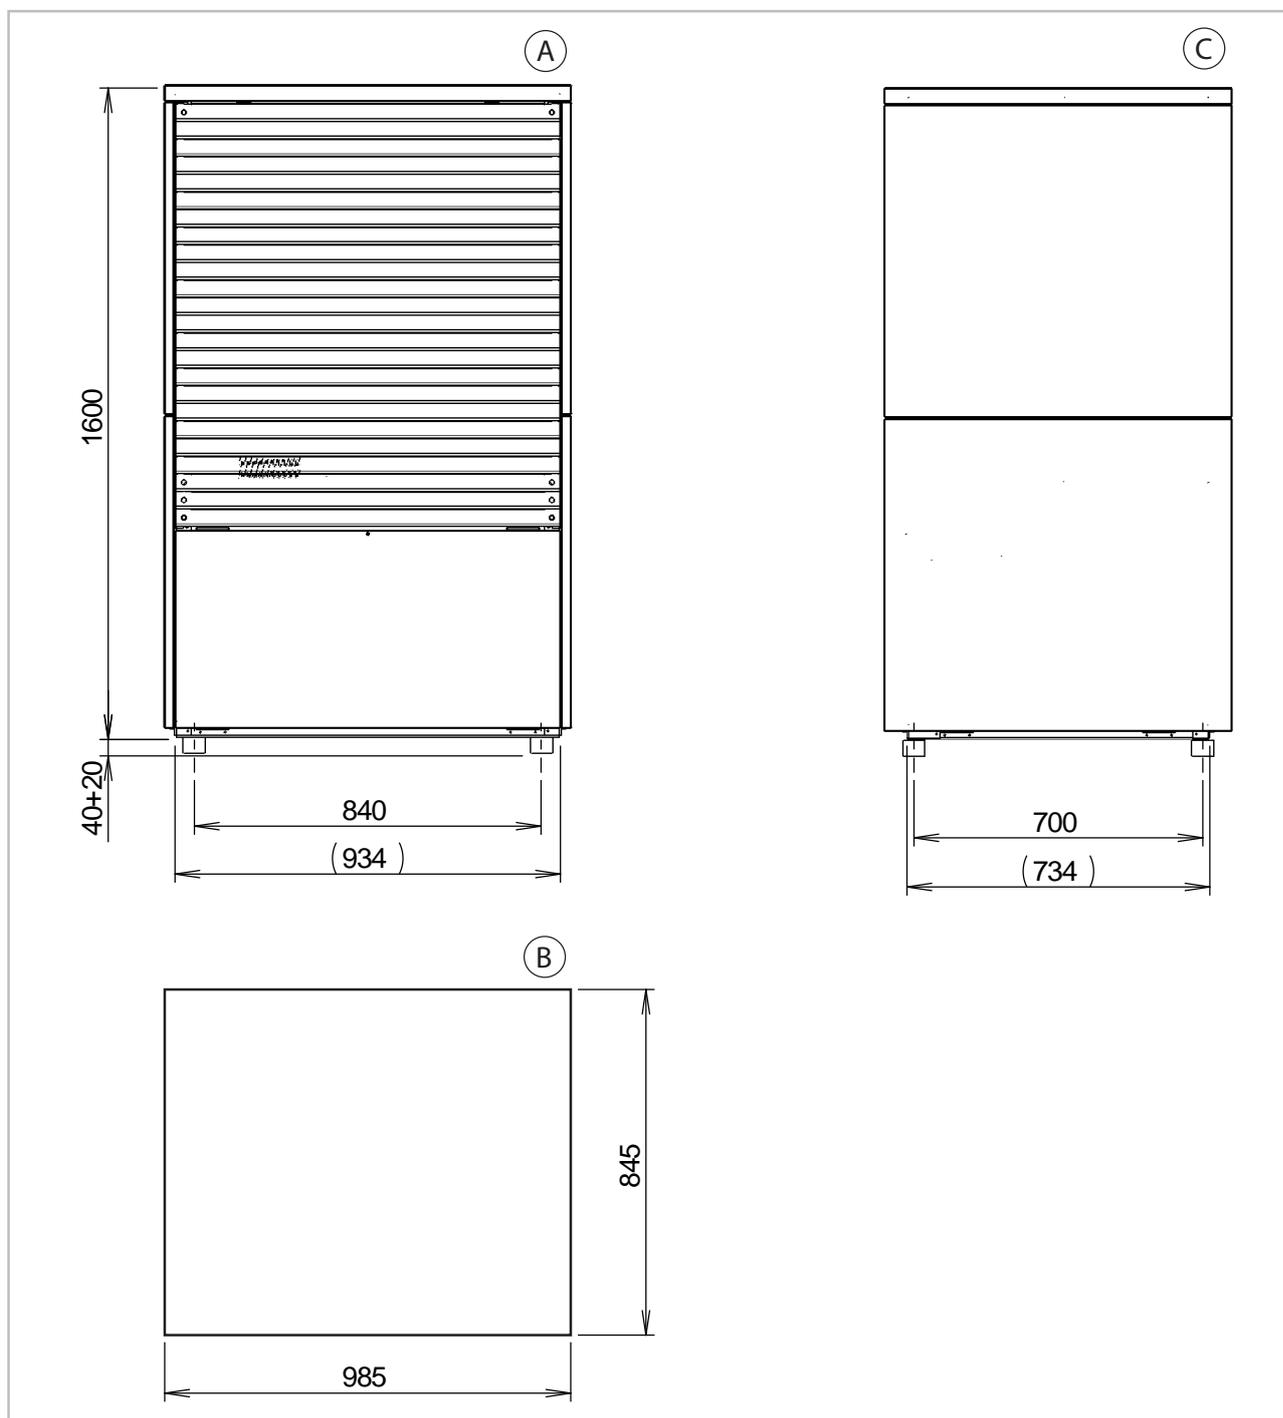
Dimensions de l'appareil (toutes les dimensions sont en mm)
